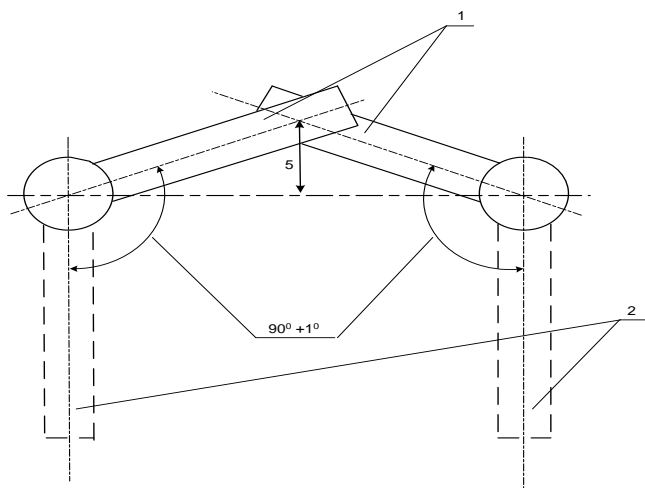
Положение контактных ножей разъединителя типа РЛНД-35/1000
